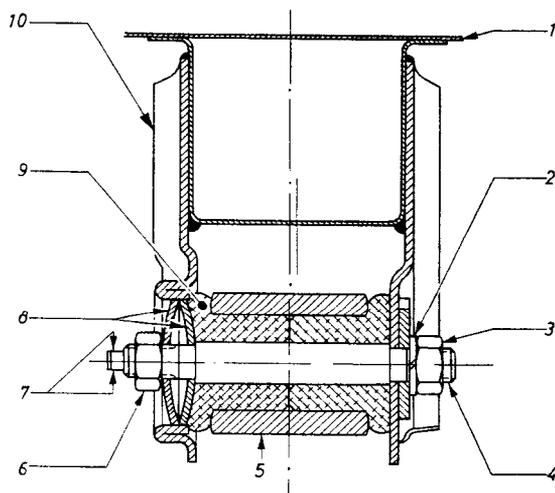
Linke vordere Hinterfederaufhängung bei einer Hinterachse mit kleinem vorderem Federauge - Ansicht in Fahrtrichtung
